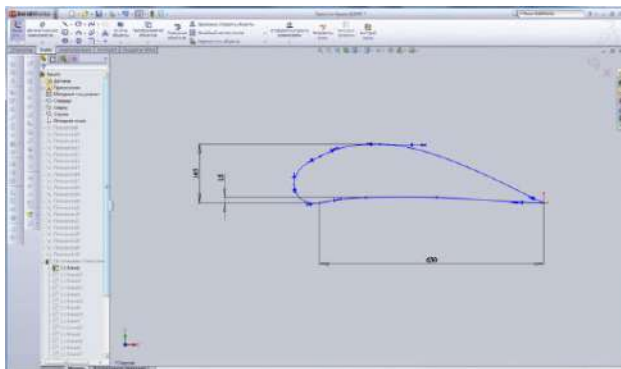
Эскиз сечения бокового профиля (боковой части) крыла
